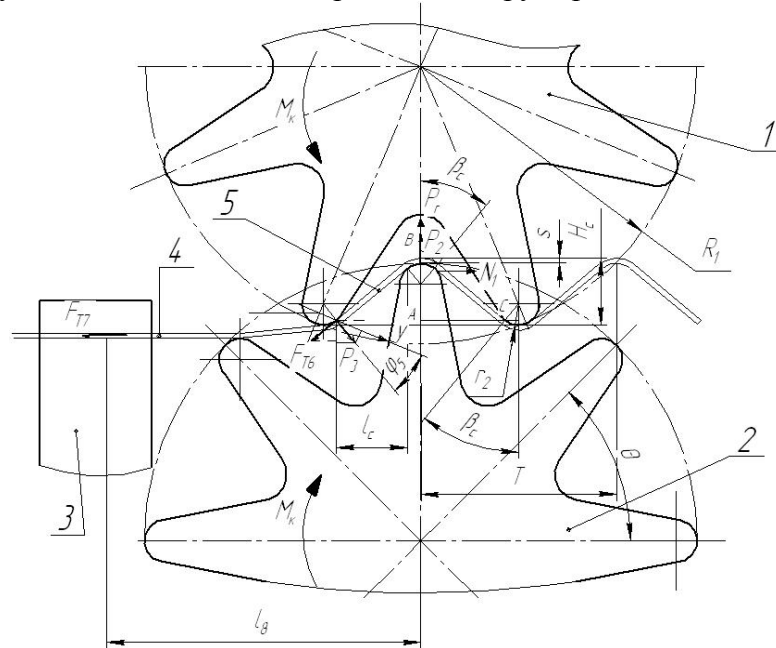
Розрахункова схема процесу формоутворення гофр на стрічці: 1 – верхній формувальний інструмент; 2 – нижній формувальний інструмент; 3 – напрямна; 4 – стрічка; 5 – профільна стрічка
